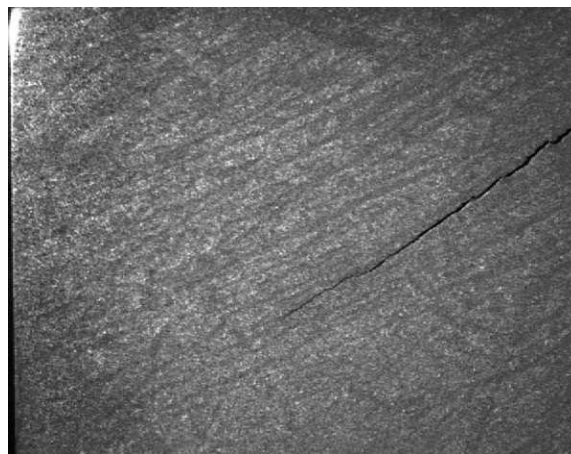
detail okují a částečného oduhličení v okolí vad, vzorek 2
